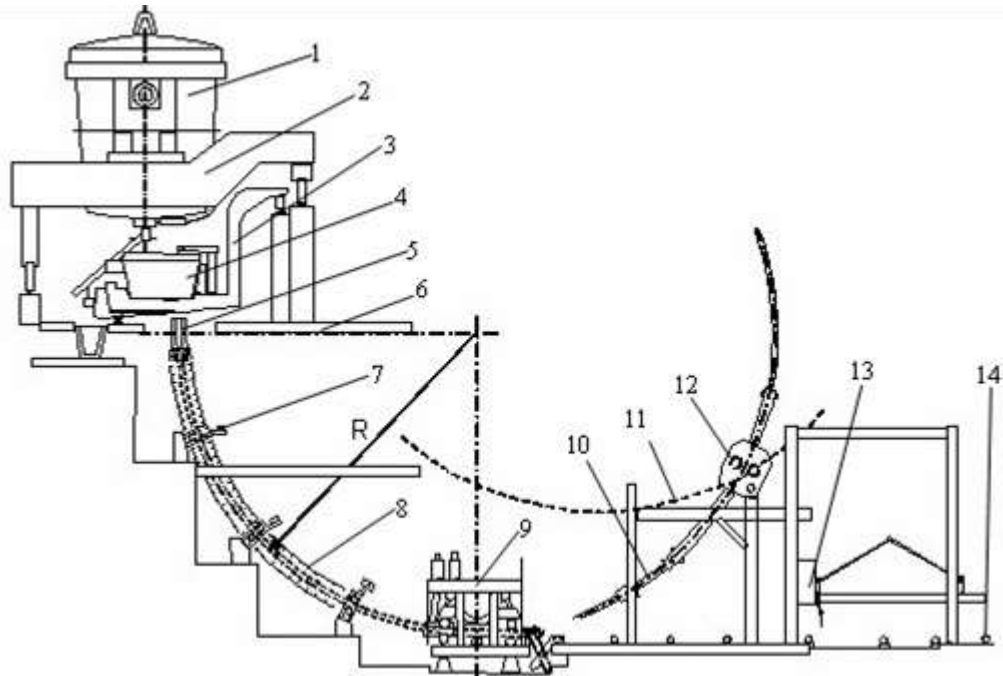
Схема охлаждения и поддерживающей системы сортовой заготовки:
